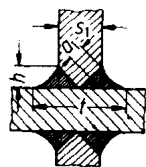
十字接头双面焊缝的 DHV (k 型) 型焊缝
